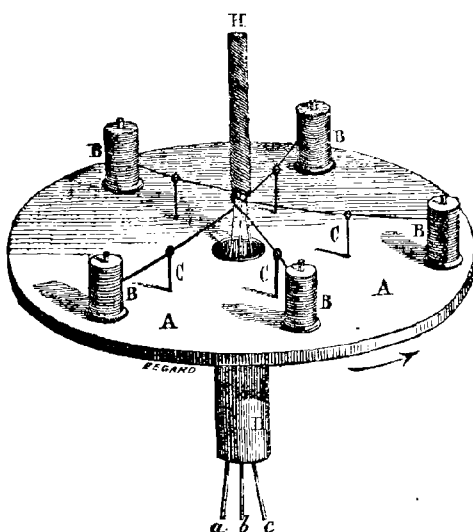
Bobine servant à la construction des câbles sous-marins.
